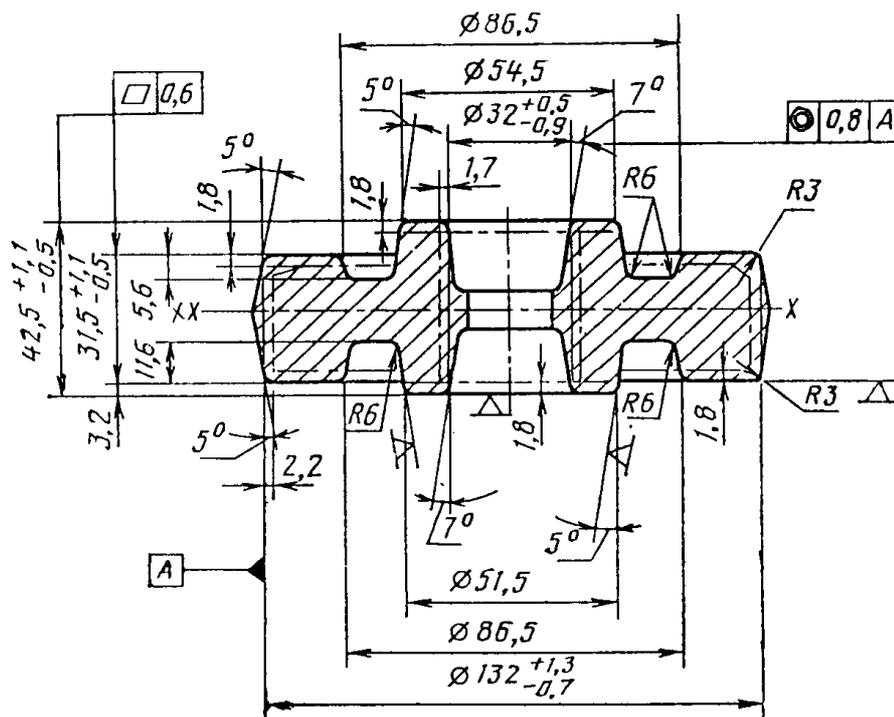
Совмещенный чертеж детали с заготовкой
